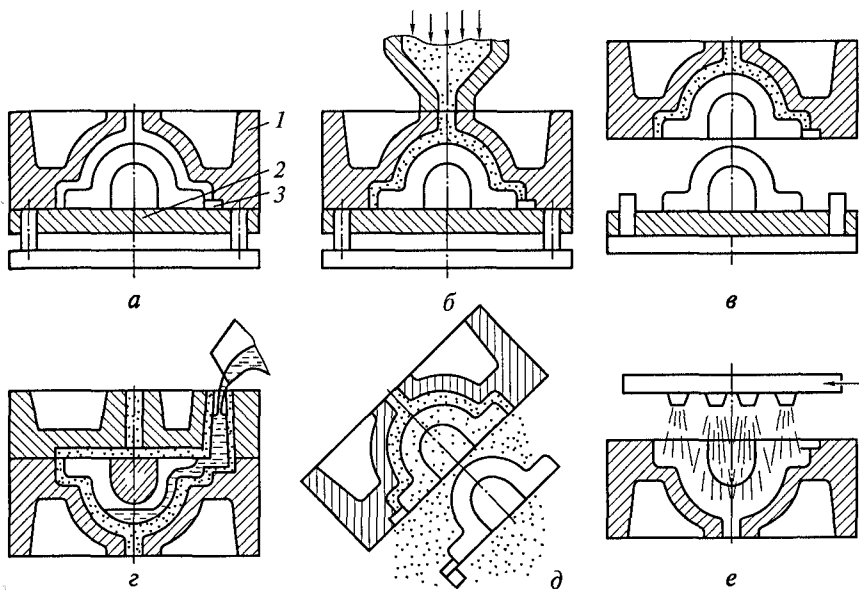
Последовательность изготовления отливки в облицованном кокиле:
